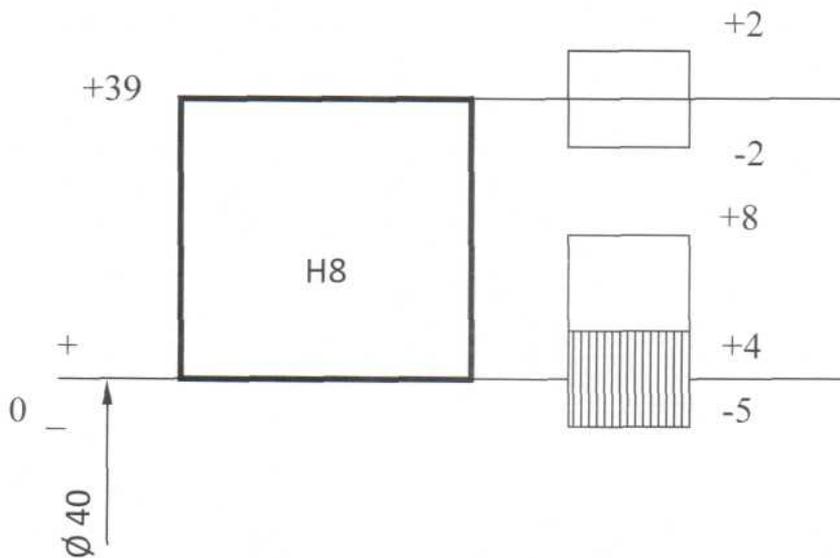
Схема полей допусков калибра-пробки для контроля отверстия $\varnothing 40$ H8
